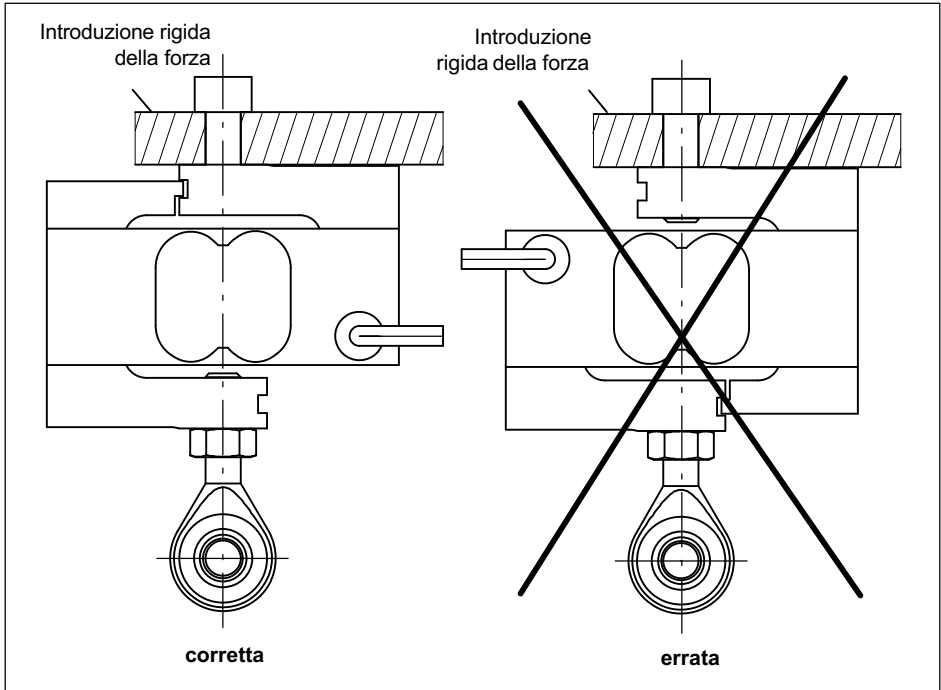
Orientamento del trasduttore durante il montaggio
